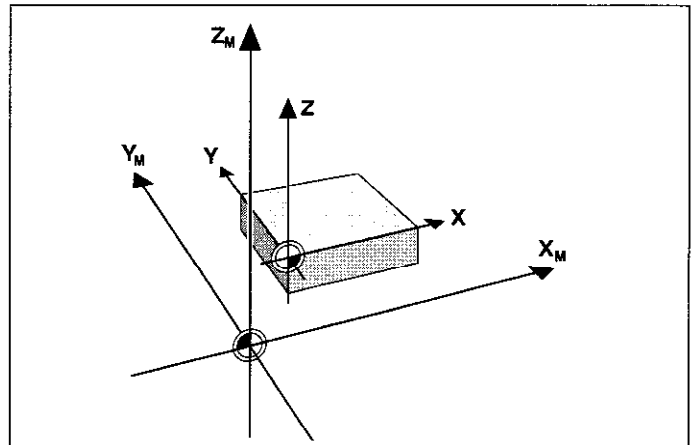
Maschinen-  und Werkstück-Nullpunkt
